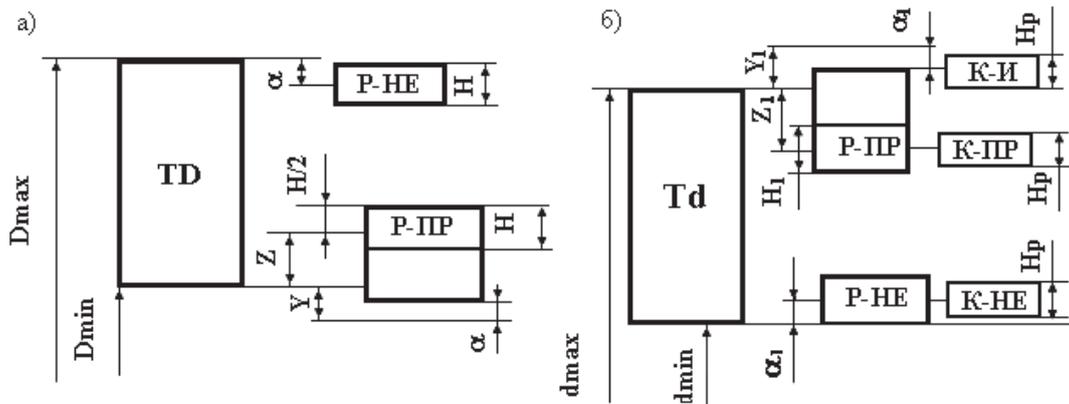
Схема расположения полей допусков предельных калибров для отверстий и валов при размерах более 180 мм:
